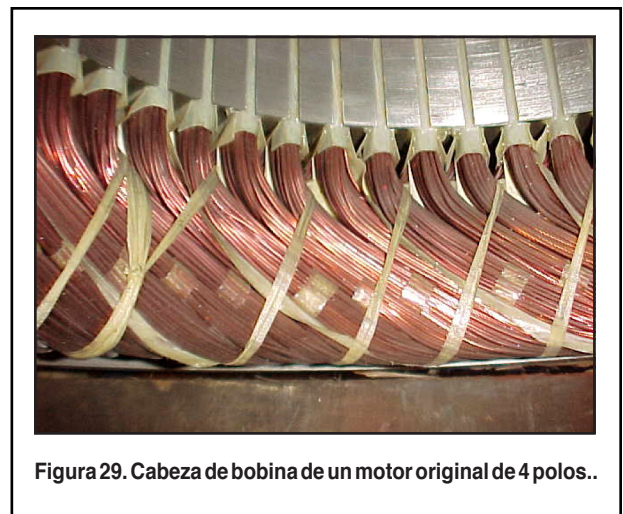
Cabeza de bobina de un motor original de 4 polos..
